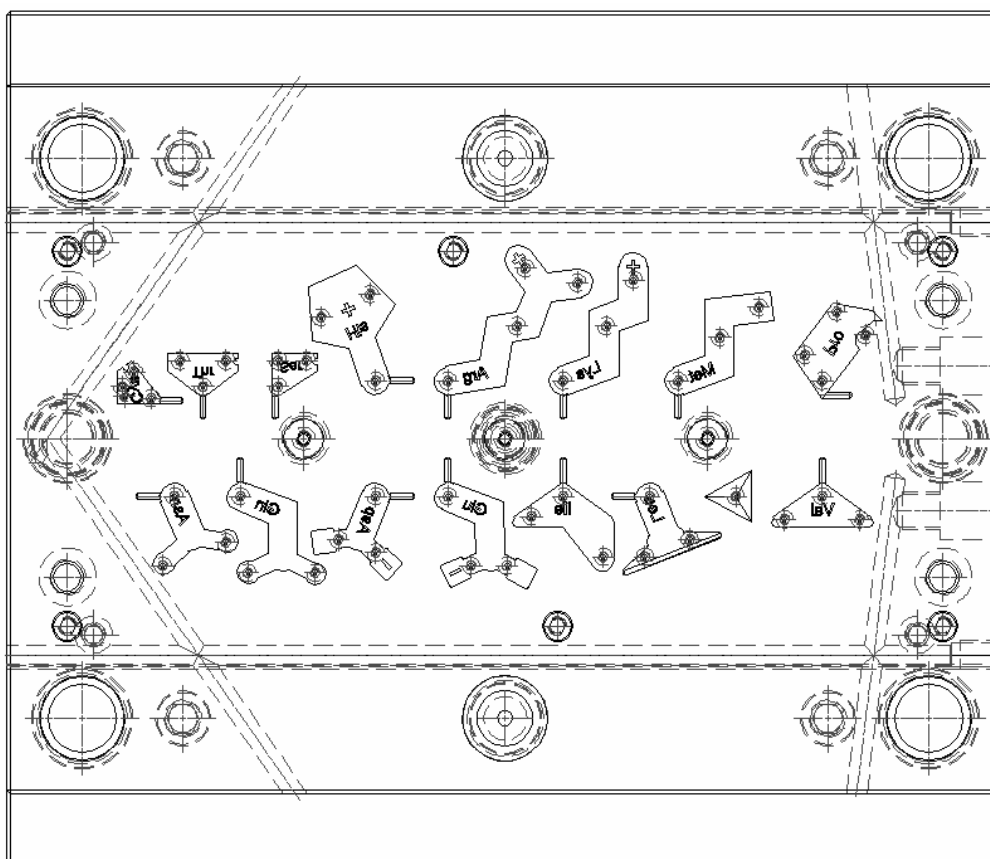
Molde para injetar a unidade representativa de 16 cadeias laterais: desenho técnico da vista superior do lado móvel
